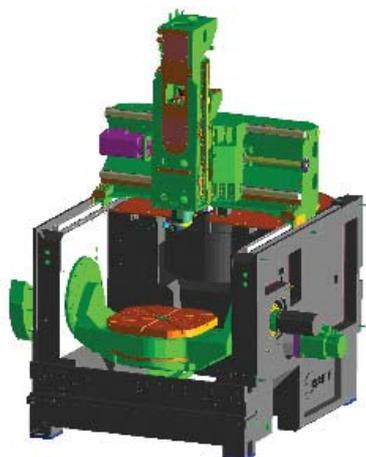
3D-модель кинематической схемы ОЦ Hermle
